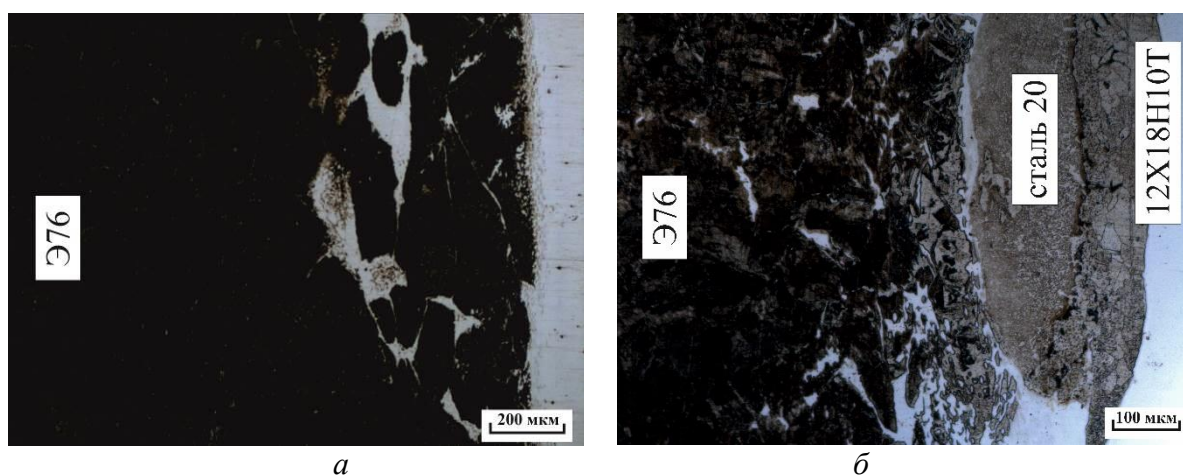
Общий вид сварного шва между сталями Э76 и 12X18H10T, сваренных без вставки – а и через низкоуглеродистую вставку толщиной 20 мм – б
